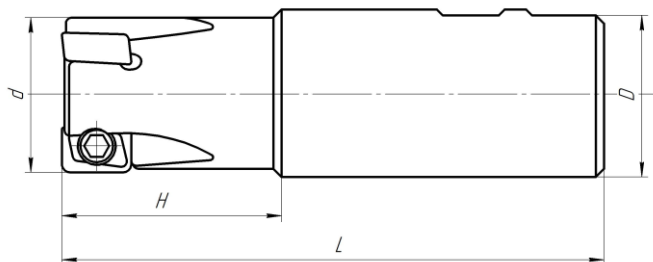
Кінцева фреза Н490 E90AX-3-W20-09
